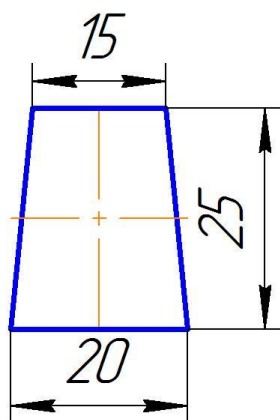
Схематичне зображення поперечного перерізу
